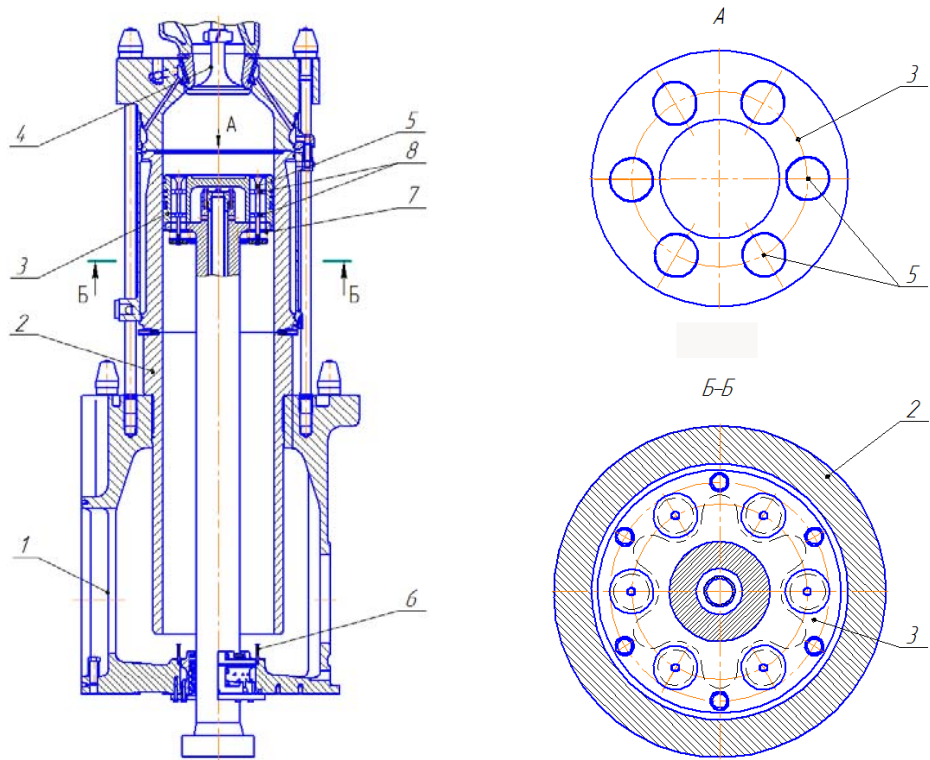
Загальний вигляд прямоточно-клапанної системи газообміну двотактного дизеля: 1 - ресивер продувного повітря; 2 - циліндрова втулка; 3 – поршень; 4 - випускний клапан; 5 - продувні клапани; 6 – упори; 7 - пружини; 8 - крилатки
